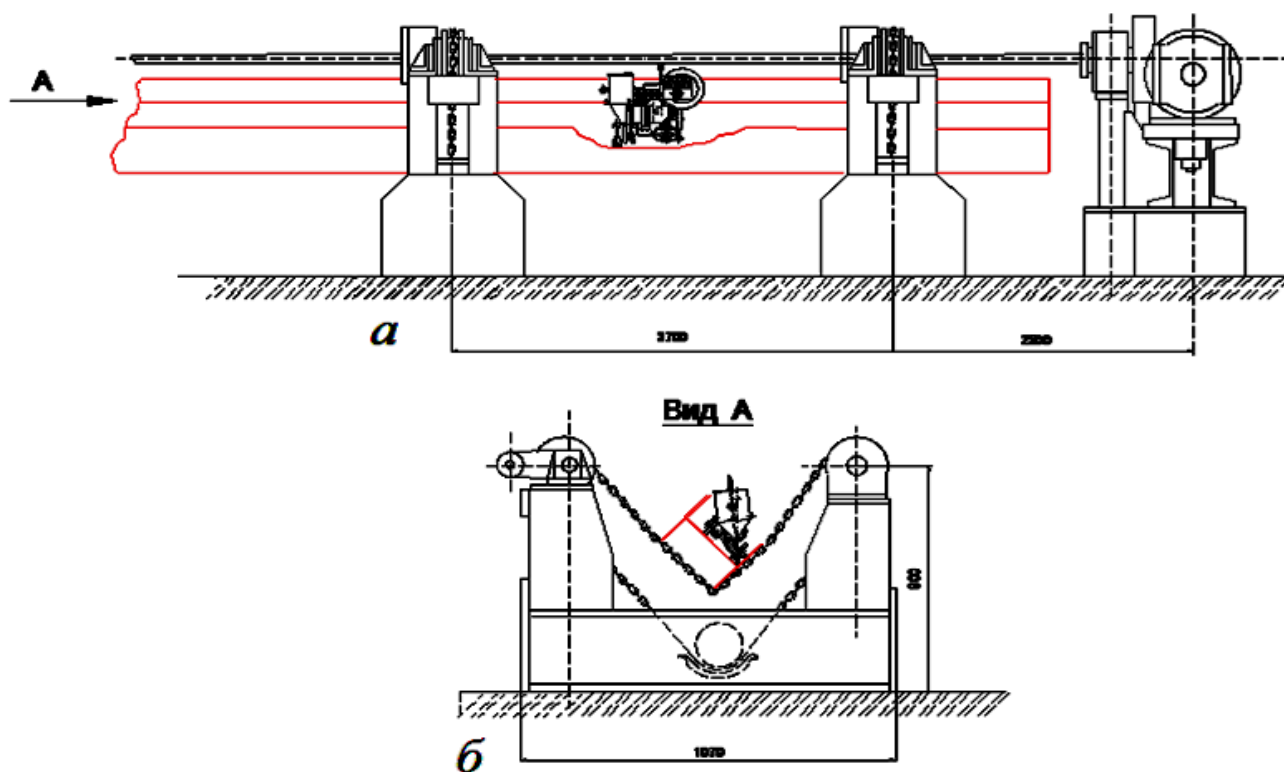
Установка для зварювання поясних швів балок за допомогою зварювального трактора та кантувача:
